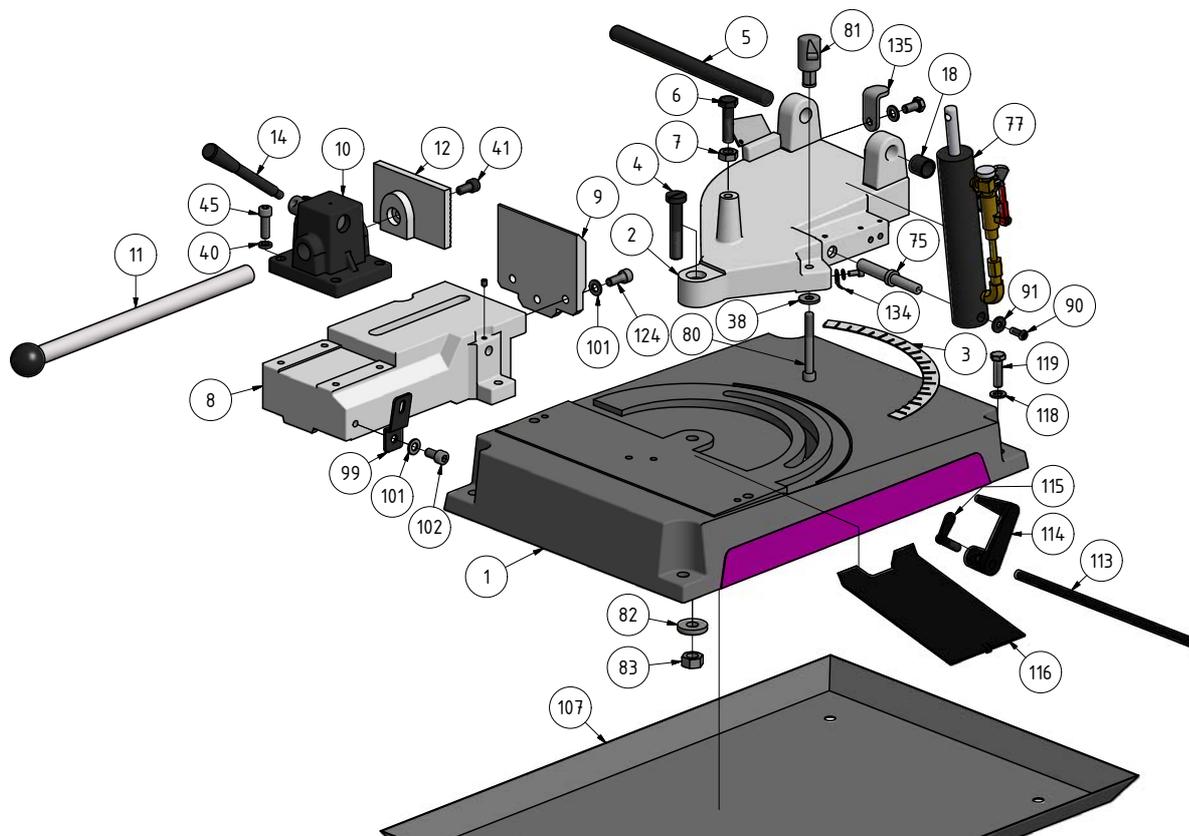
Ersatzteilzeichnung 3 von 4 - Parts drawing 3 of 4
